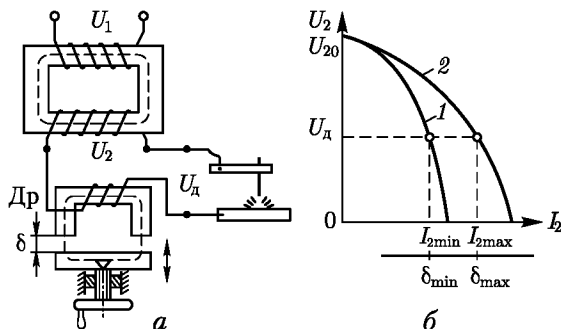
Схема включения (а) и внешние характеристики (б) трансформатора для электродуговой сварки
